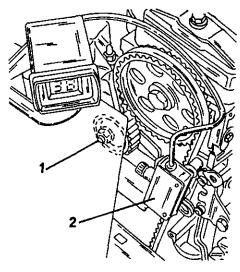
Использование измерительного прибора для натяжения зубчатого ремня на двигателе типа TU.
